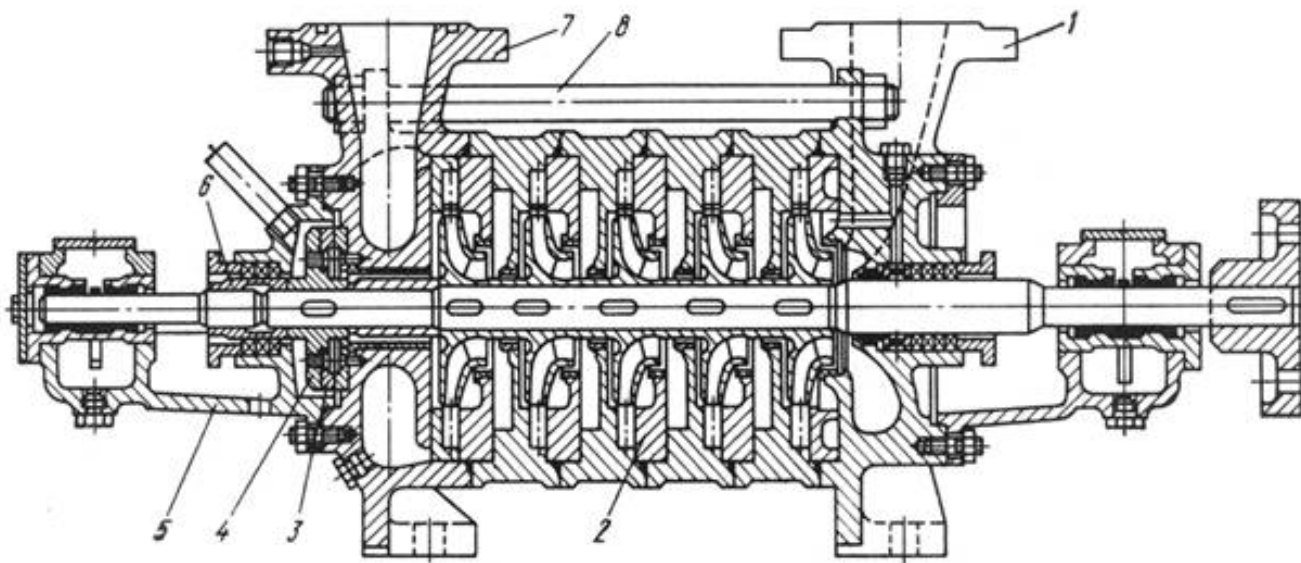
Насос секционного типа: 1 – всасывающий патрубок, 2 – секция; 3 – разгрузочная пята, 4 – разгрузочный диск; 5 – кронштейн подшипника, 6 – защитная втулка вала; 7 – напорный патрубок, 8 – стяжная шпилька
